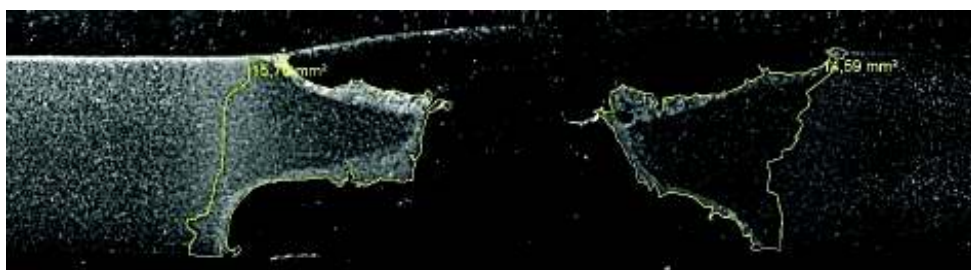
Área de la ZAC en cada región del cordón de soldadura
